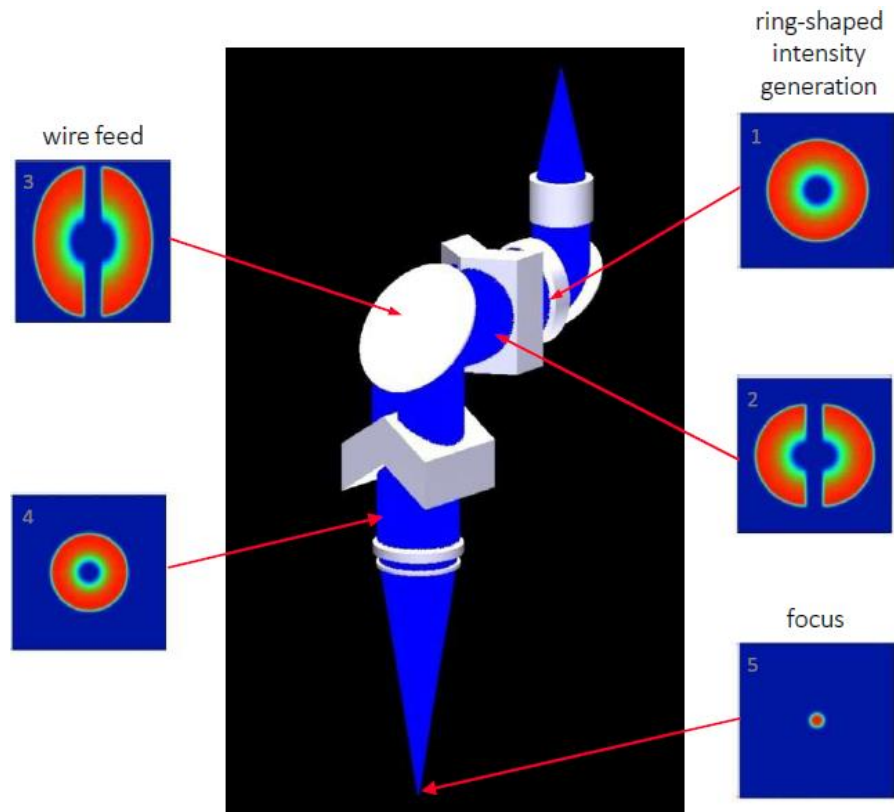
Fraunhofer IWS, koaxiální hlava COAXwire [55]
